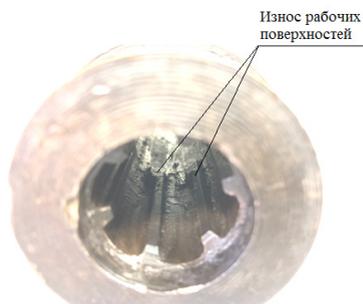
Изношенная втулка редуктора трактора МТЗ 82
